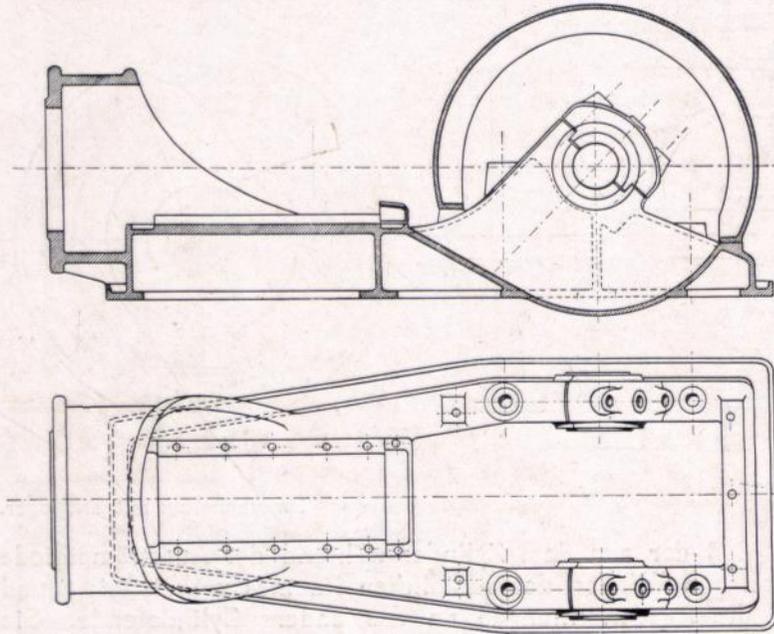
Grundplatte für gekröpfte Welle mit Flachführung.
